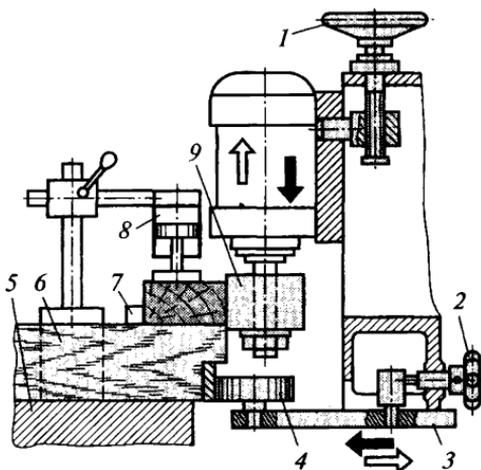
Настройка копирного ролика карусельного фрезерного станка:
